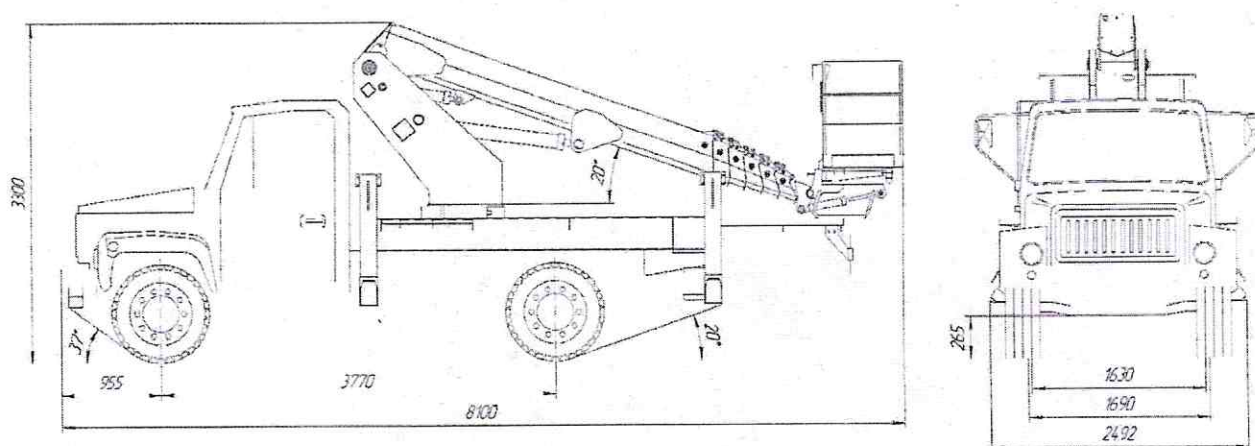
Габаритные размеры подъемника ВИПО-24-01
